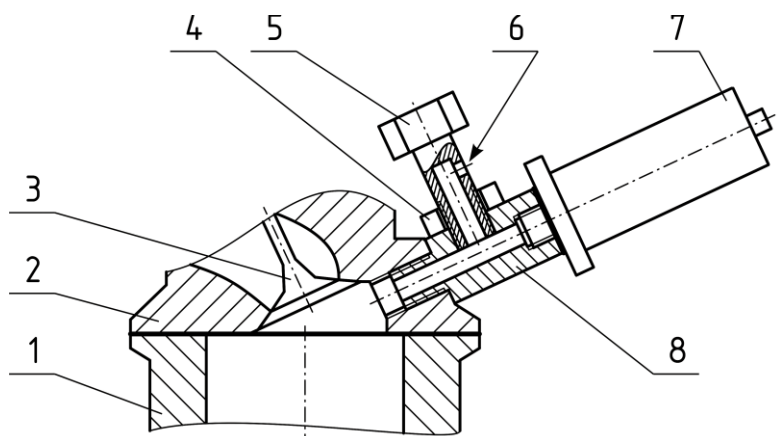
Схема для имитации негерметичности камеры сгорания: 1 – блок цилиндров; 2 – головка блока цилиндров; 3 – клапан; 4 – гайка; 5 – болт; 6 – калибровочное отверстие; 7 – датчик давления; 8 – переходник
